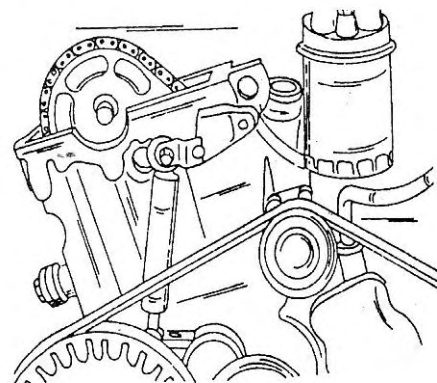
Отвернуть амортизатор устройства натяжения ремня только от головки цилиндров.
